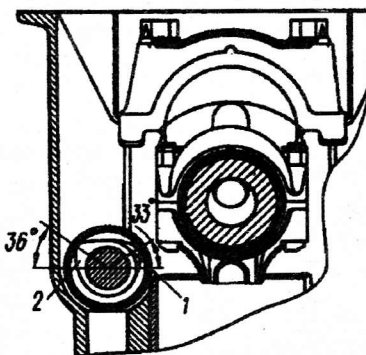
Положение кулачков распределительного вала первого цилиндра при установке привода датчика-распределителя зажигания:
